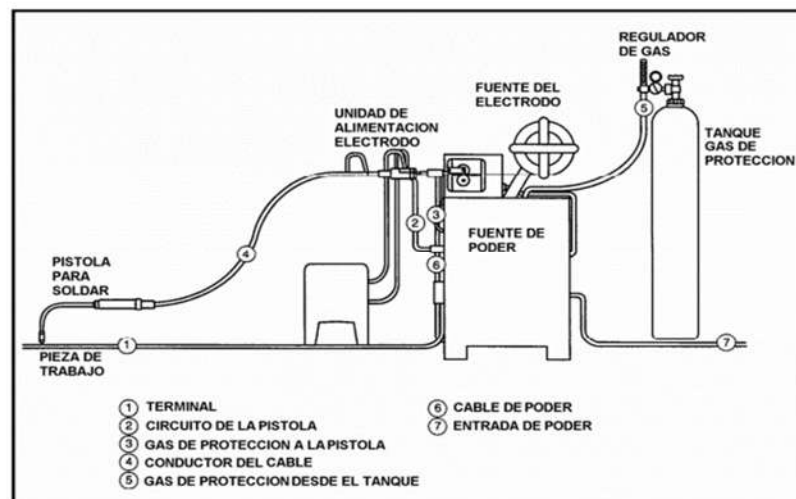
Esquema del equipo del proceso de soldadura GMAW [8].
